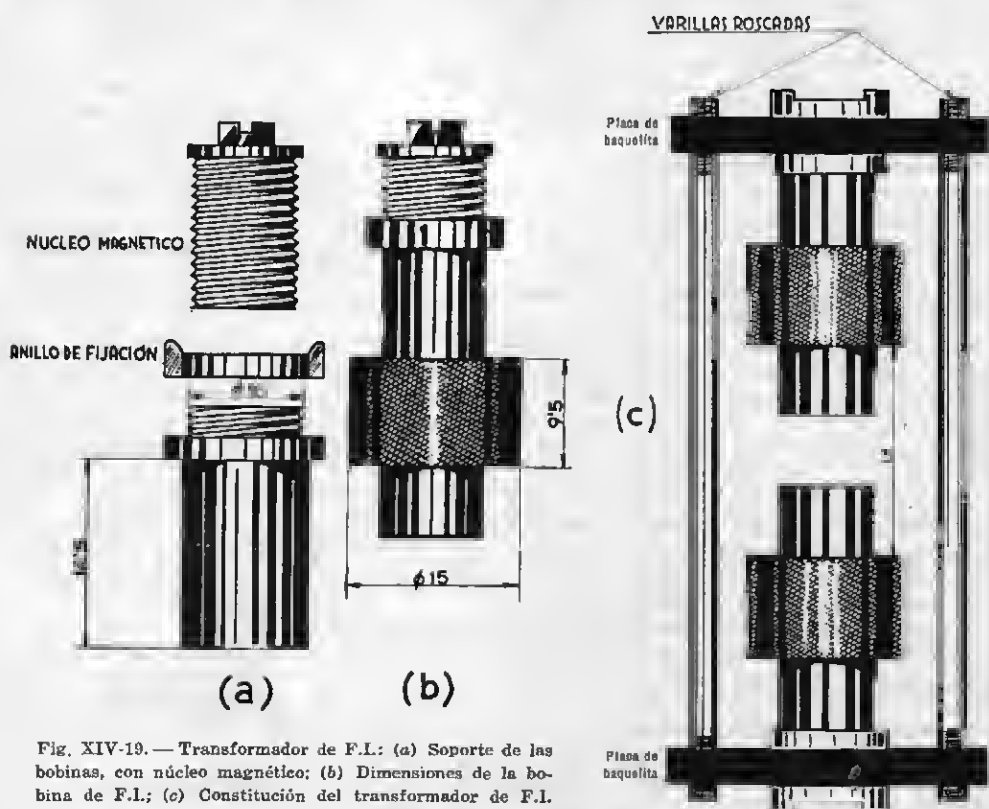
Transformador de F.L.: (a) Soporte de las bobinas, con núcleo magnético; (b) Dimensiones de la bobina de F.L.; (c) Constitución del transformador de F.L.
